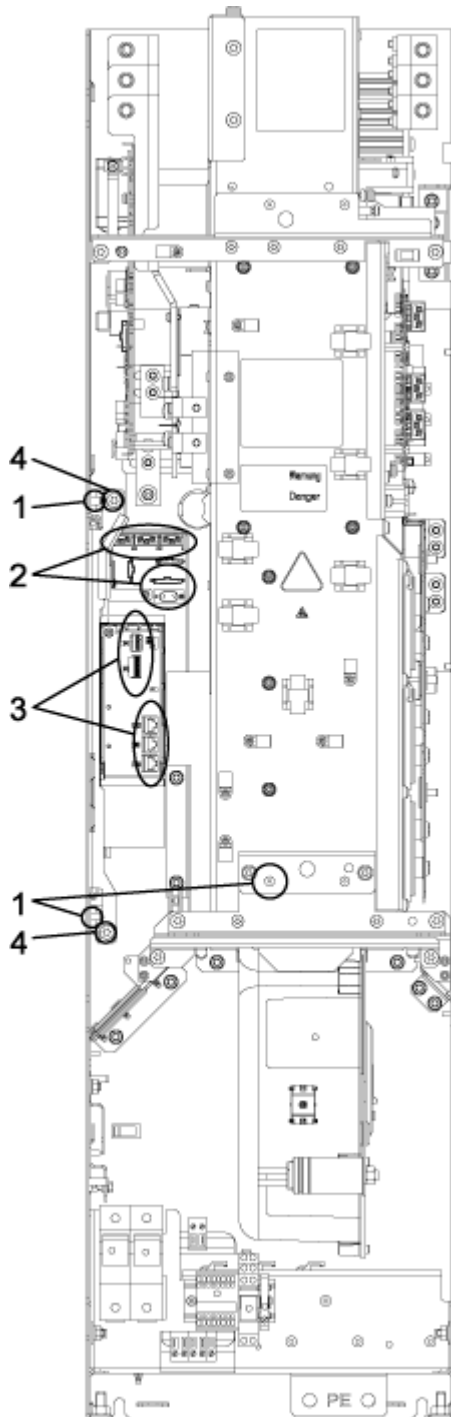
Austausch Control Interface Board, Baugröße FX
